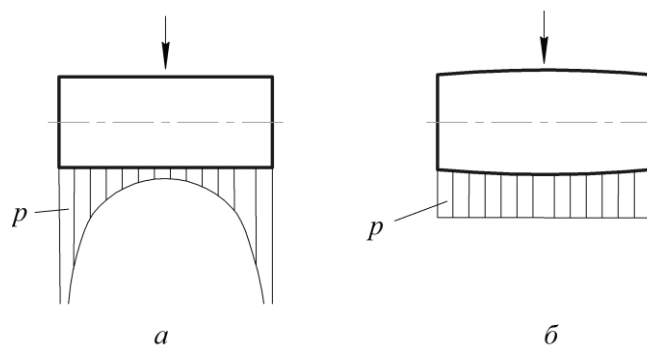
Распределение рабочих давлений p вдоль образующей при контакте ролика и поверхности катания: а – при цилиндрической форме; б – при бочкообразной форме
